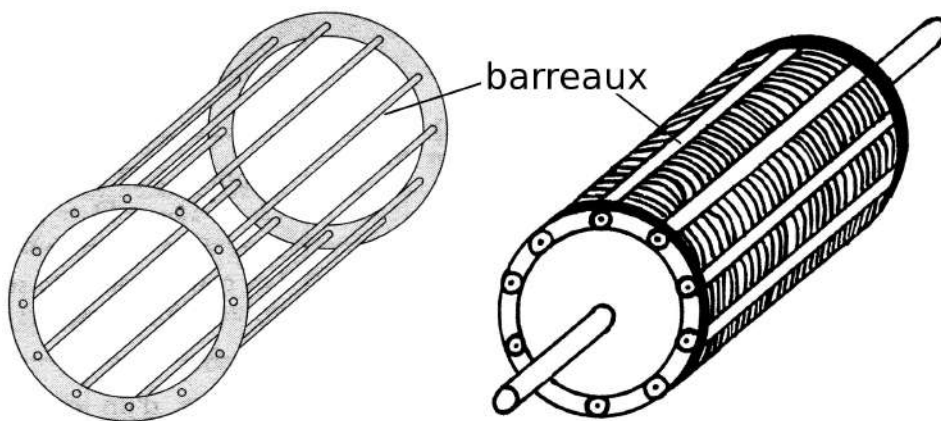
rotor à cage d'écureuil, la cage vide de fer à gauche et emplie de rondelles de fer à droite.
